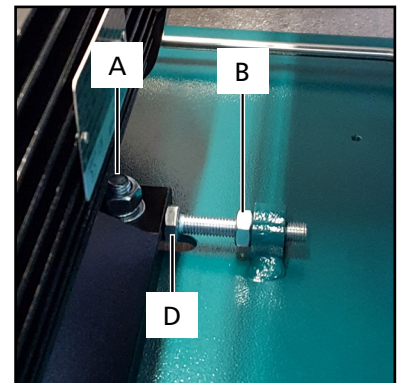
Befestigungsmutter (A) (4x), Kontermutter (B), Ausrichtschraube (D)
